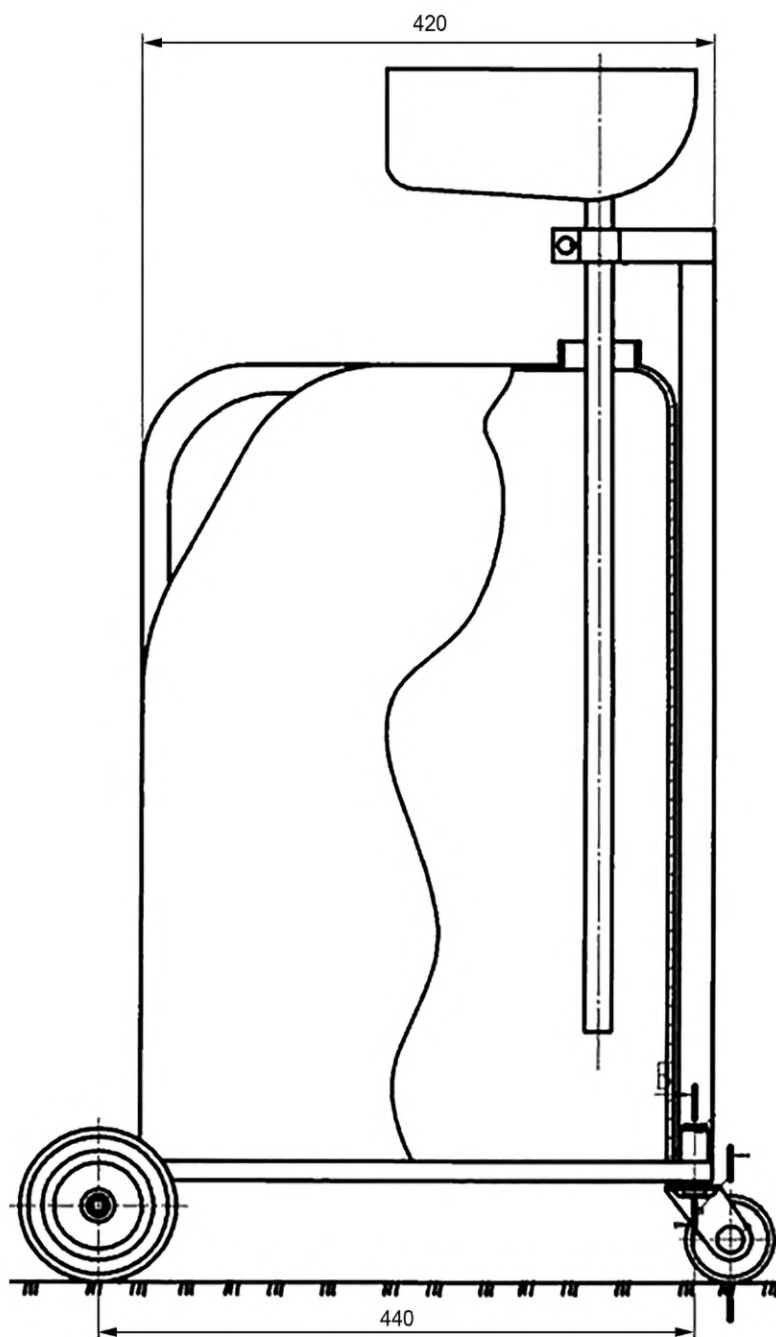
Тележка под канистру для слива и перевозки горюче-смазочных материалов
